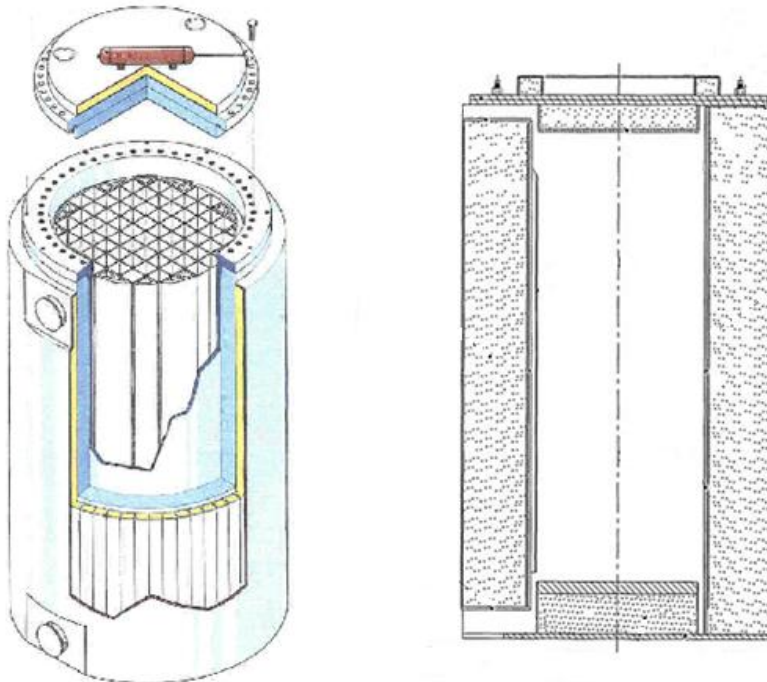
Vertikaler Lagerbehälter mit verschraubtem Deckel und mit geschweißtem Deckel
